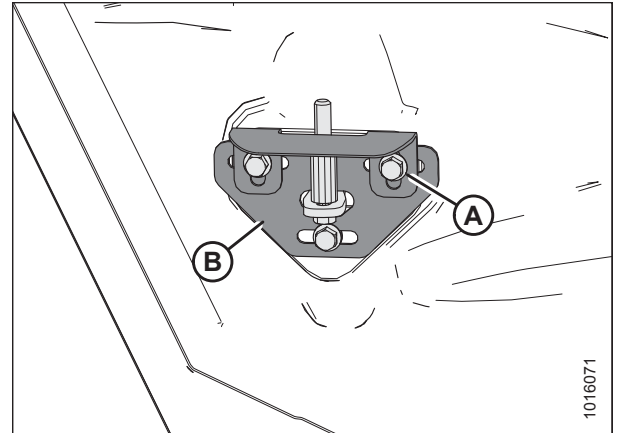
Ensemble du loquet du capot du diviseur gauche
